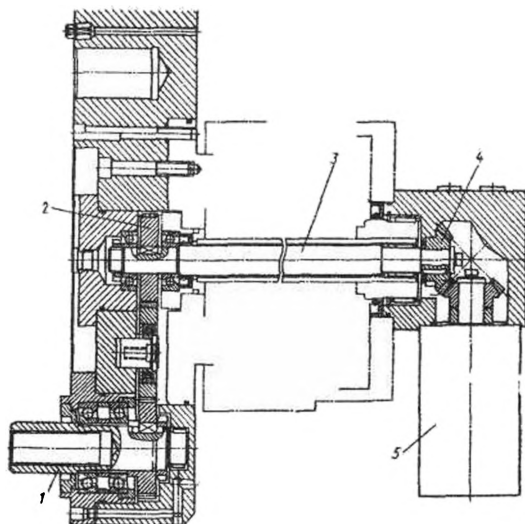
Револьверна головка з рушієм для обертання шпинделів з інструментами
